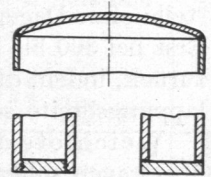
bis 609. Unrichtige Lage der Schweißnähte, die starken Nebenbeanspruchungen auf Zug und Biegung ausgesetzt sind.
